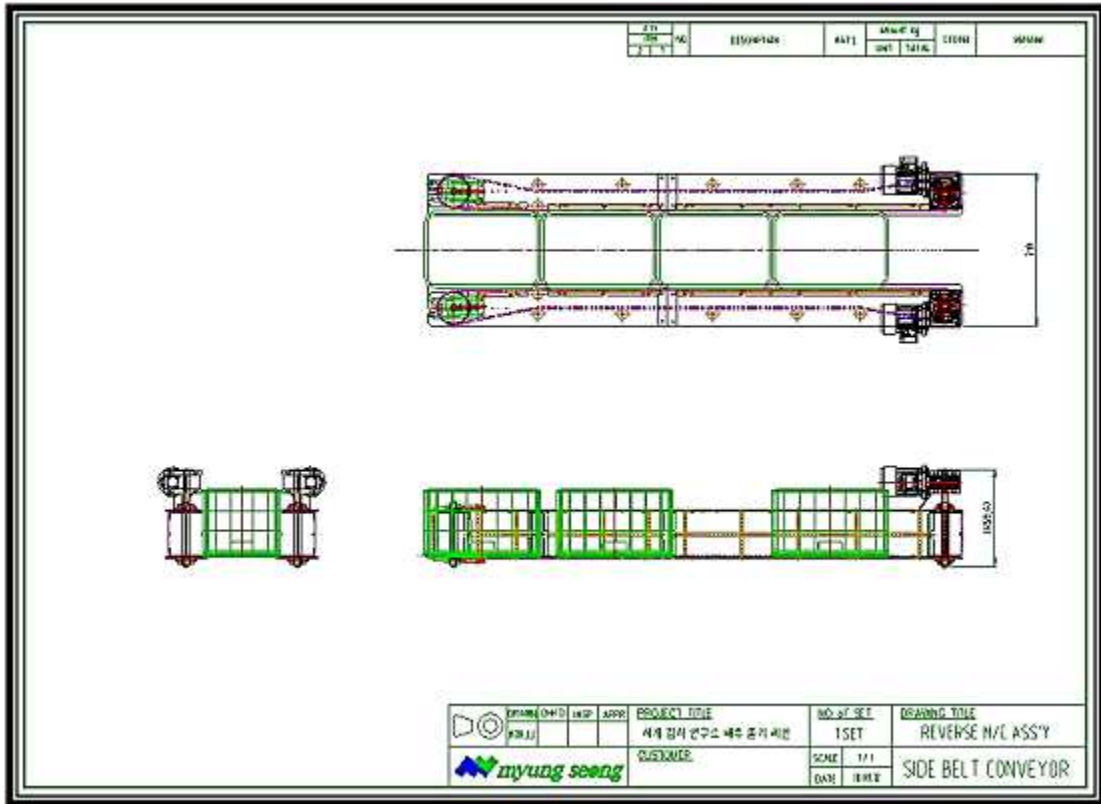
Side belt conveyor - 반전 상자 배출 conveyor
